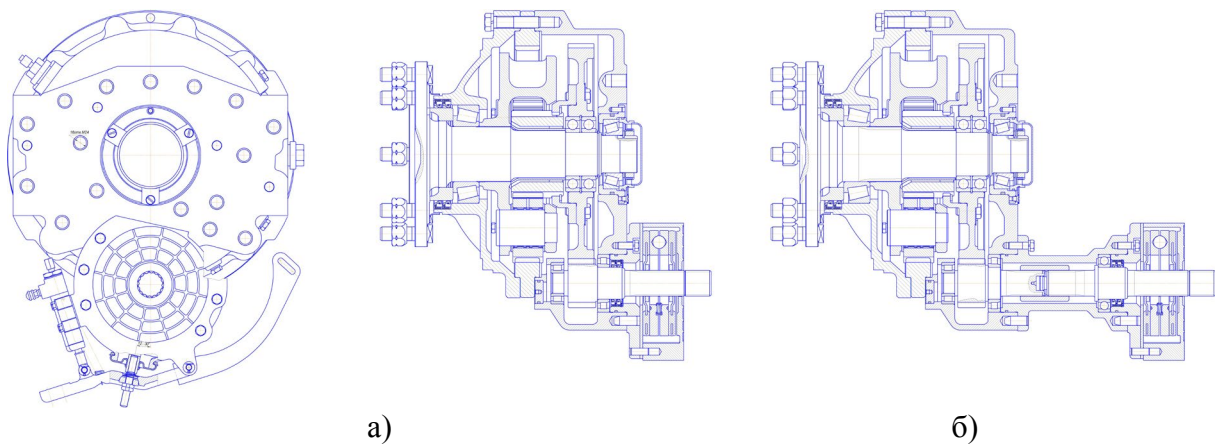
Бортовий редуктор базової (а) та удосконаленої (б) конструкції
